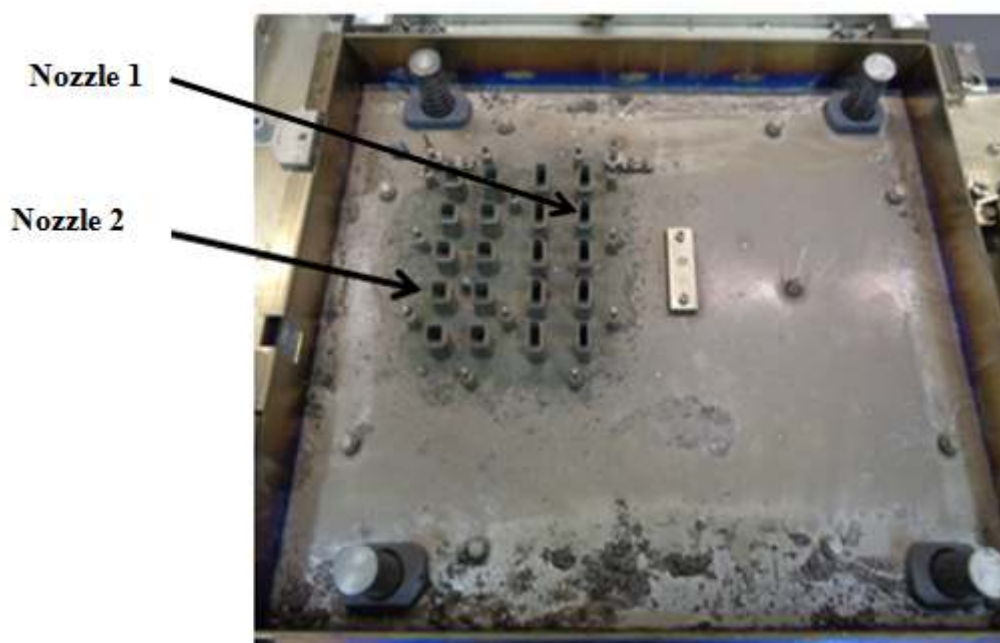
Ferramenta utilizada na soldagem seletiva.
